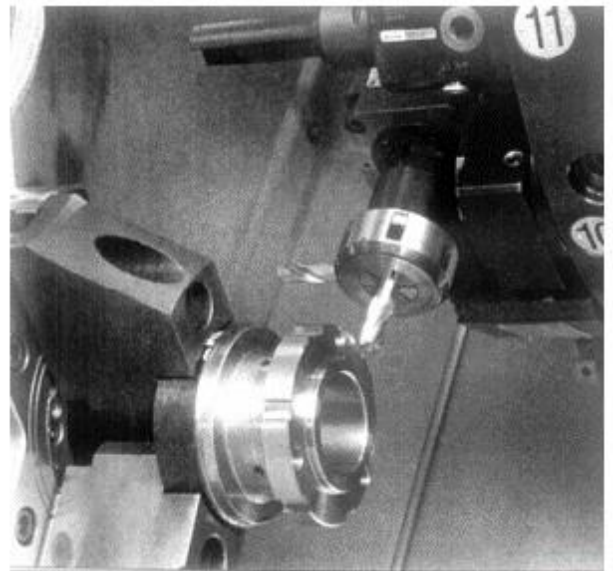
Загальний вигляд револьверної головки до верстата із ЧПК із нахиленою станиною.
